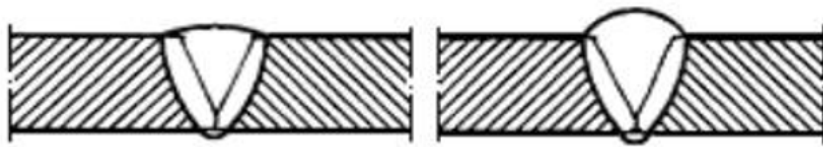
Эскиз дефекта сварного шва
